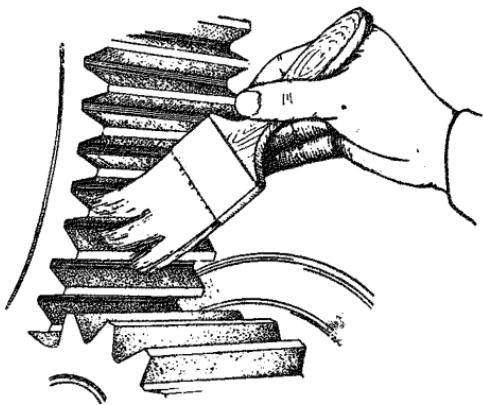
Смазка открытых зубчатых передач при помощи кисти
